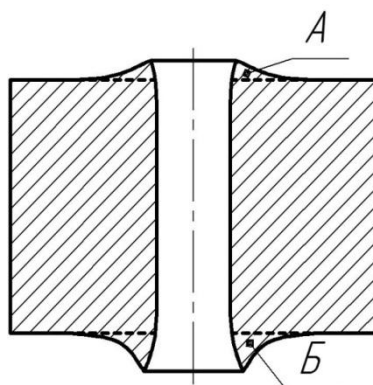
Схема наплывов металла на торцах заготовок, обработанных дорнованием: A – входной торец; B – выходной торец
